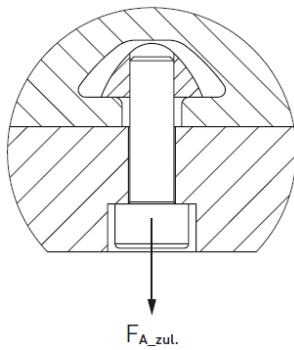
Befestigung mit Nutensteinen – HM040S, HM060S, HM080S
